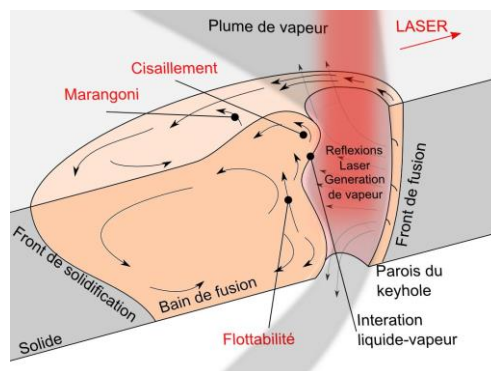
Schéma illustrant le principe du soudage laser.
